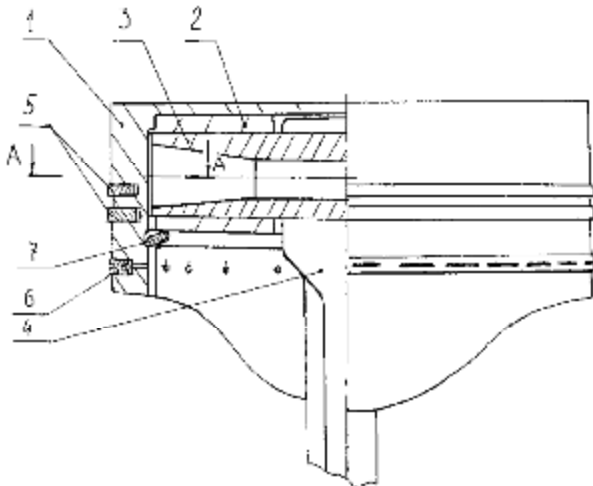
Поршень двигуна внутрішнього згоряння з тонкостінним корпусом; 1 – корпус оболонковий, 2 – вставка, 3 – палець поршневий; 4 – шатун; 5 – компресійні кільця; 6 – маслозємне кільце; 7 – стопорне кільце.
